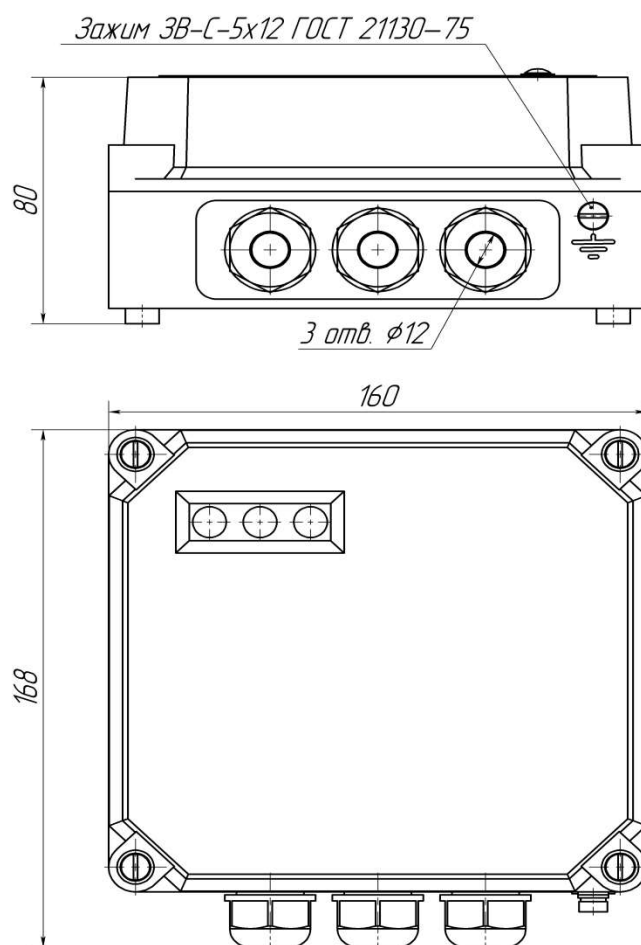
Габаритные и установочные размеры ВП
